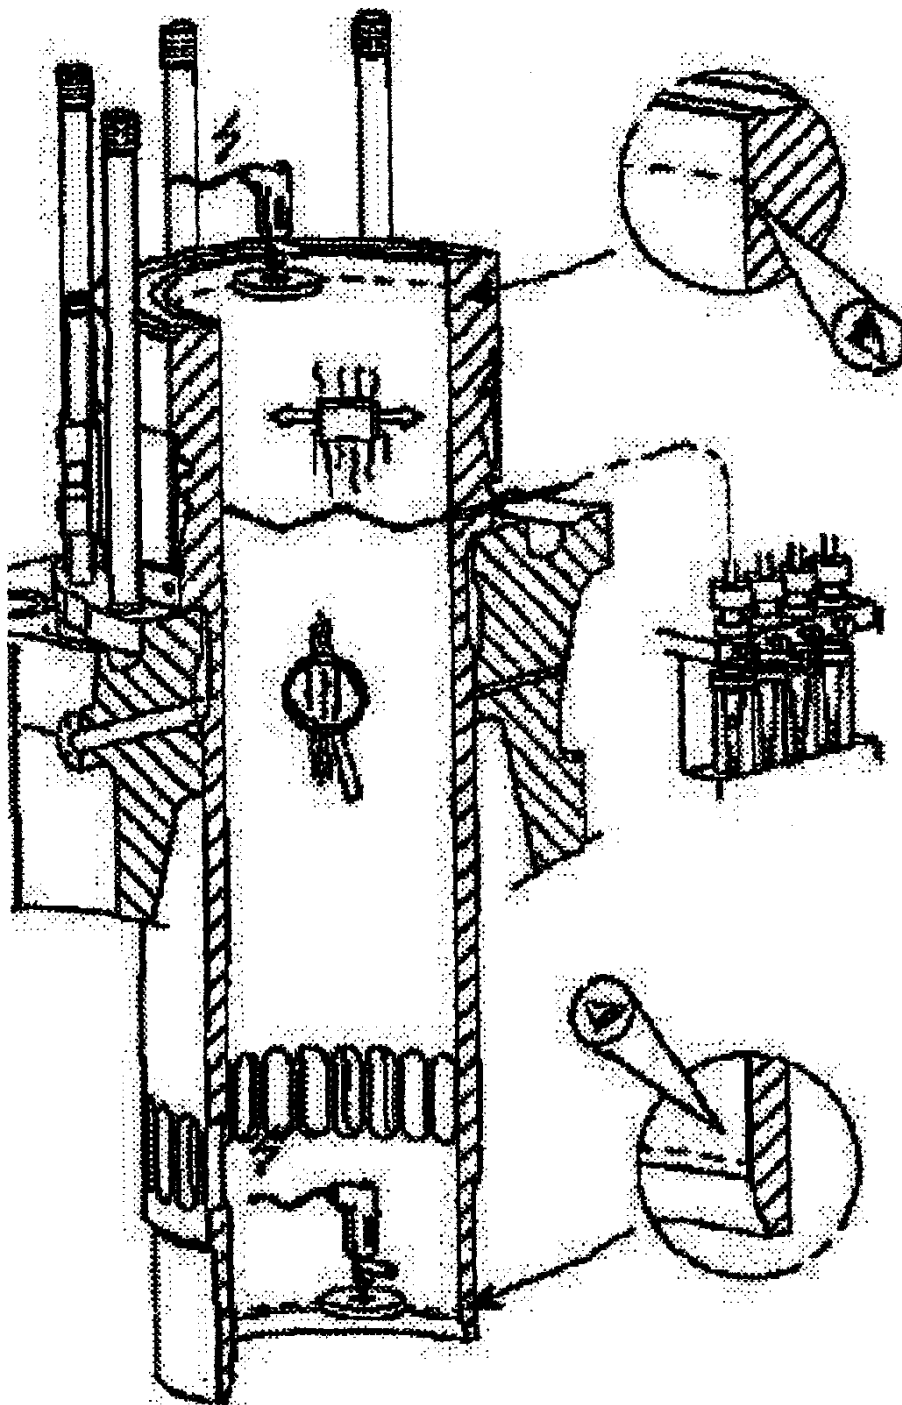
Огляд та обробка робочої поверхні втулки
